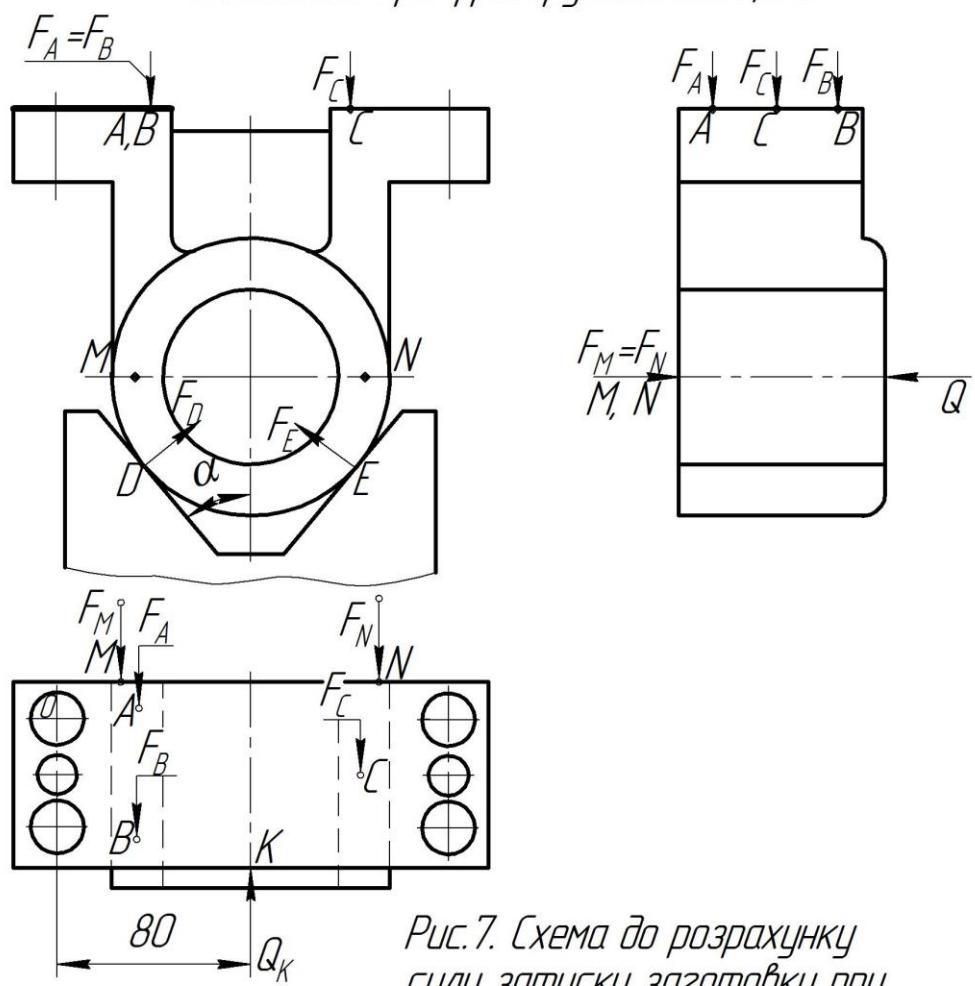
Схема до розрахунку сили заліску заготовки при свердлінні отворів
